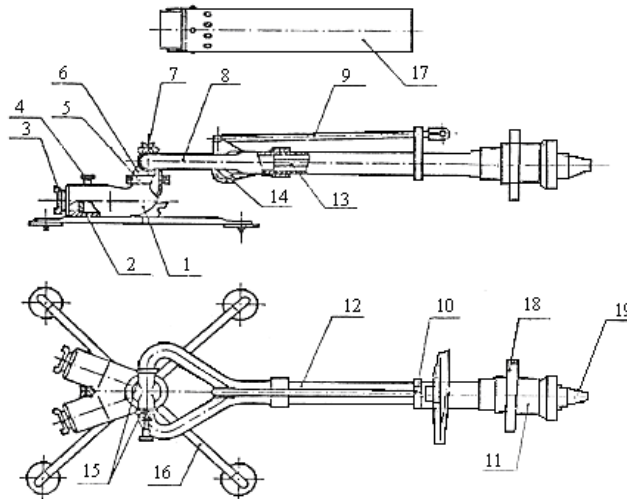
Будова ствола СЛК-П20А1 — корпус; 2 — відкидний зворотний клапан; 3 — з'єднувальна головка; 4 — відкидний болт; 5, 15 — ущільнювальний пристрій; 6 — поворотний трійник; 7 — шпindel; 8 — патрубок з розводом; 9 — відкидна рукоятка; 10 — заскочка; 11 — пристрій для утворення захисної завіси; 12 — труба; 13 — заспокоювач; 14 — пружинний фіксатор; 16 — змінна опора; 17- повітряно-пінний насадок; 18 — штурвал; 19 – насадок Ø 25, 28, 32 мм
